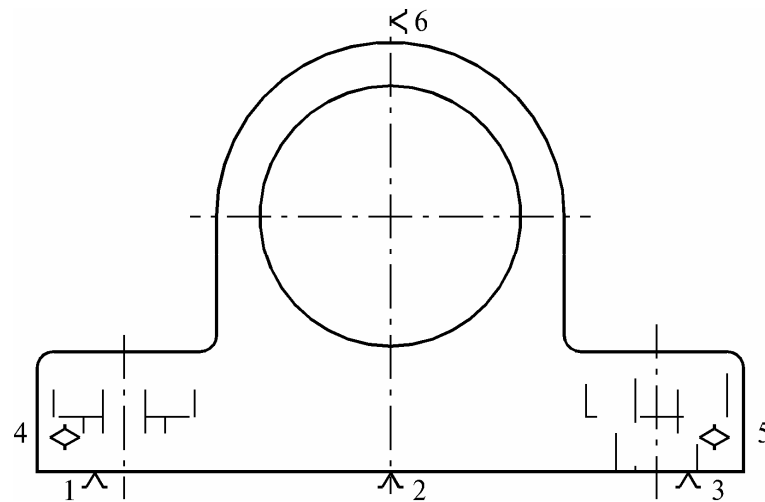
Схема базирования заготовки корпуса на большинстве операций
